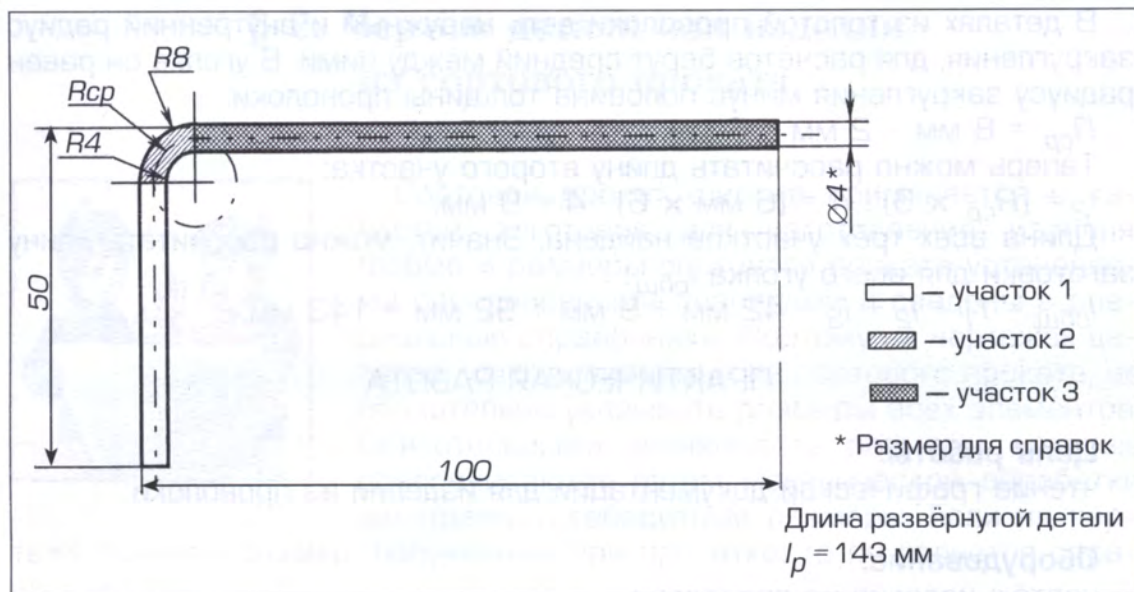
Чертёж для расчёта длины заготовки для изготовления уголка из проволоки
